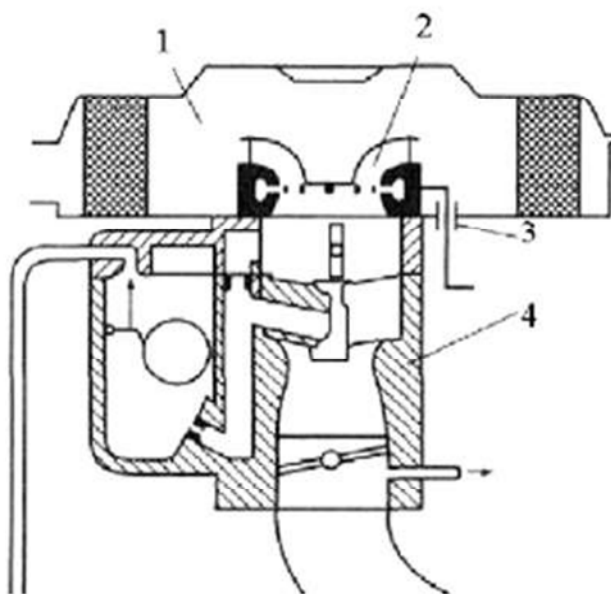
Схема подачи газа над карбюратором: 1 - воздушный фильтр; 2 - смеситель-насадка; 3 - отверстие для подвода газа; 4 - корпус карбюратора
